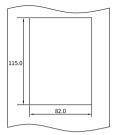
键盘安装支架 1 外形尺寸(单位:mm)
